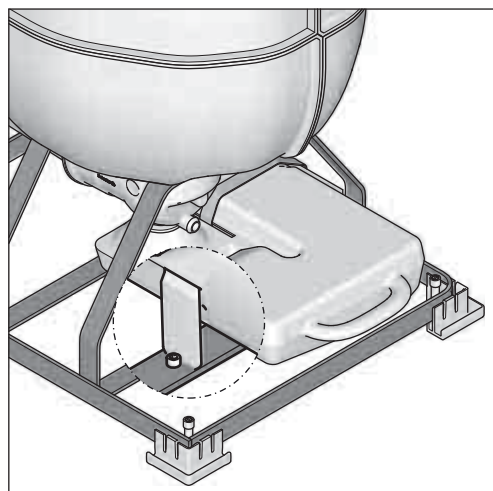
Far scattare in posizione la linguetta stabilizzante
